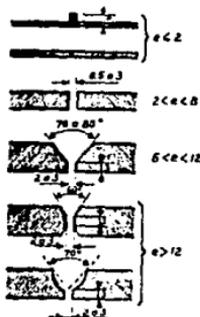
Preparación de los bordes para soldadura TIG.
